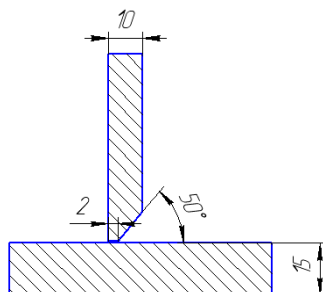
Эскиз сварного соединения Т7 по ГОСТ 8713-79
